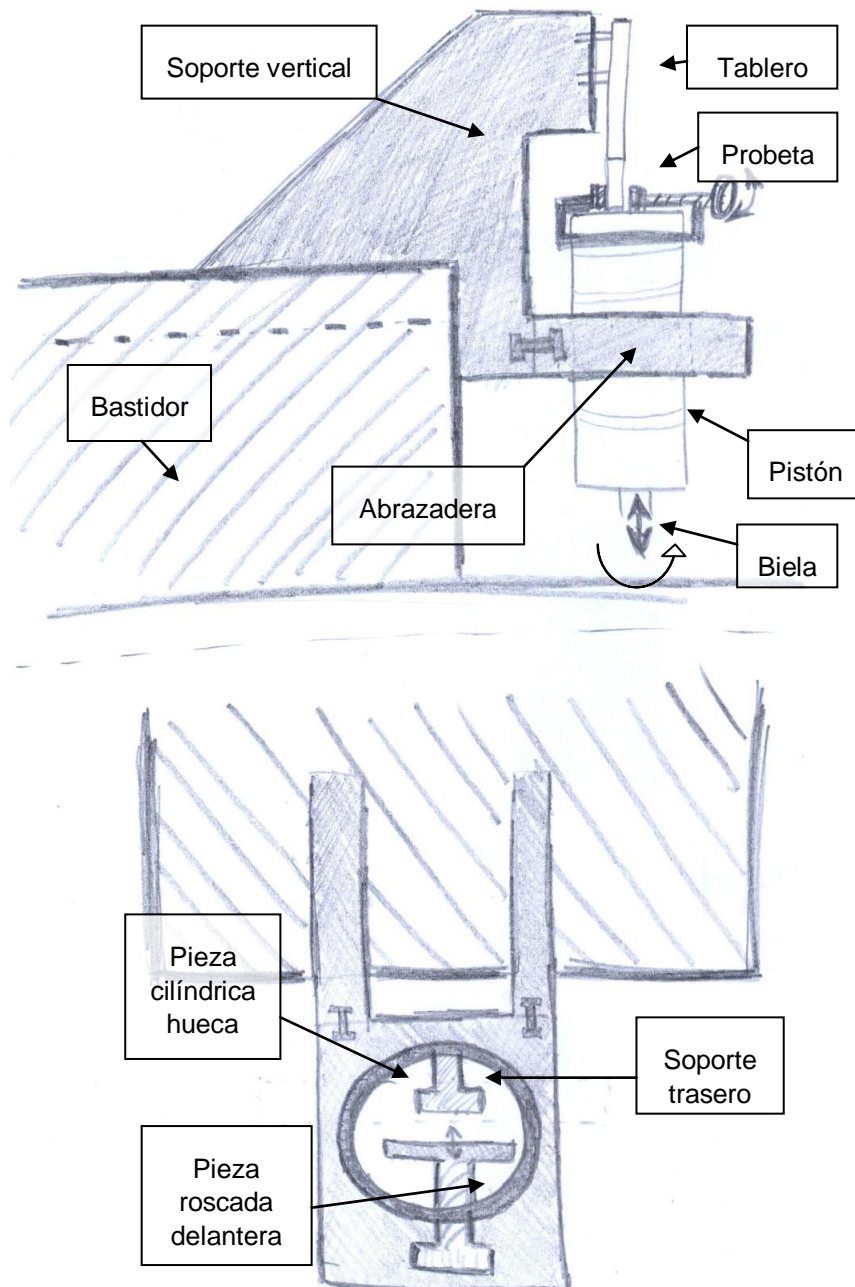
Vistas lateral y planta del prototipo B.
